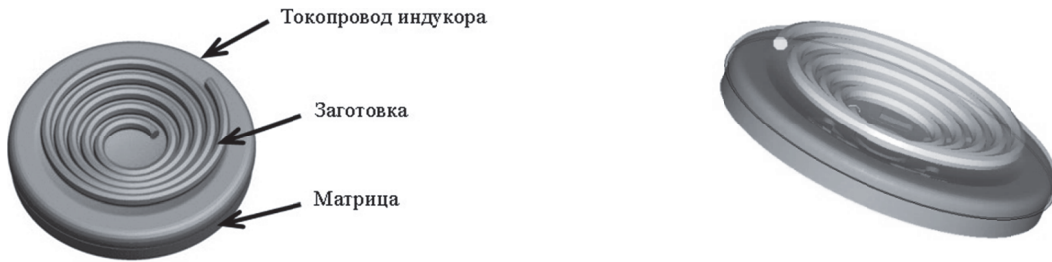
Взаимное расположение моделей заготовки, матрицы и индуктора
